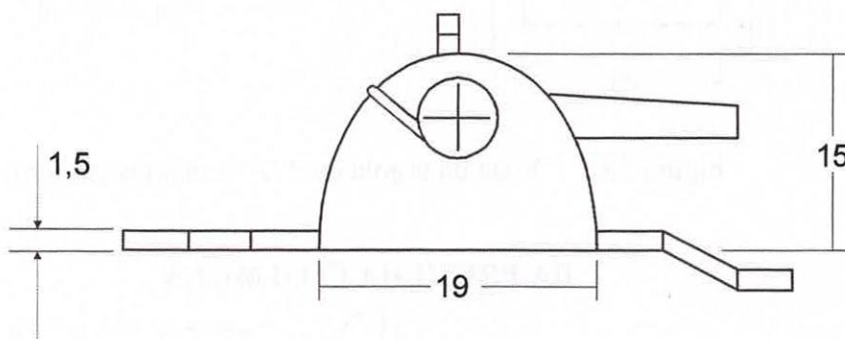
Vista lateral do ajustador metálico (medidas em mm)
